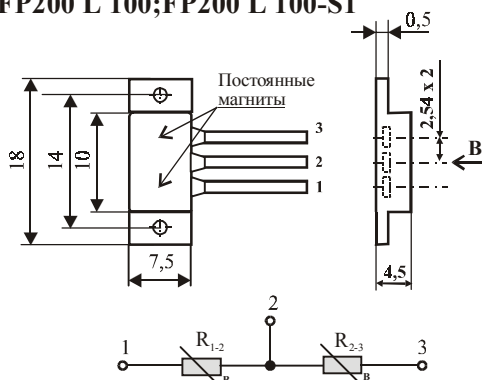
Внешний вид и габаритные размеры магниторезистора FP 100 L 100
